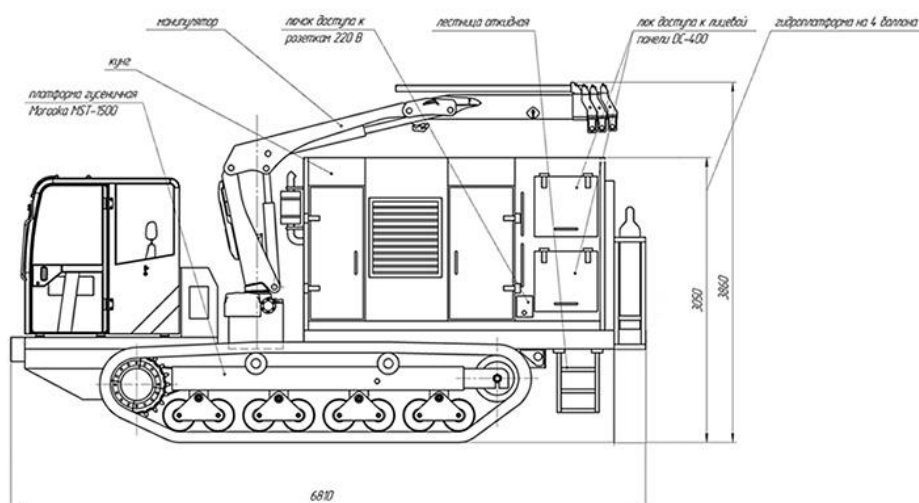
Агрегат самоходный сварочный МКСТ-34
